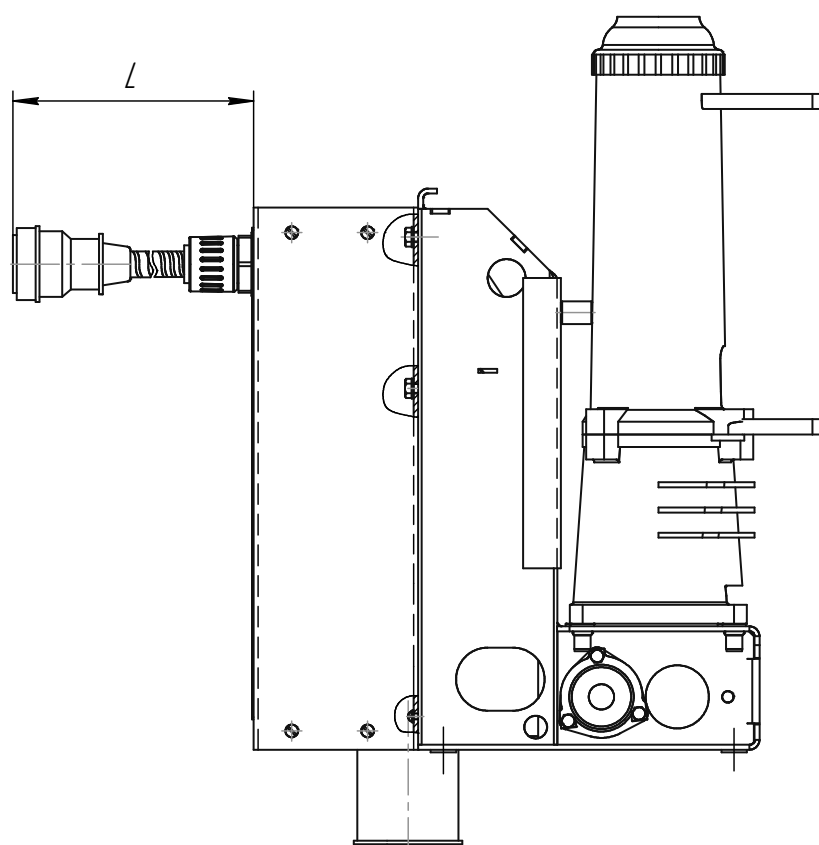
Габаритные, присоединительные и установочные размеры выключателей ВВУ-СЭЩ-ЭЗ-10-20(31,5)/ для К-26 (остальное смотреть рисунок Б.5)
